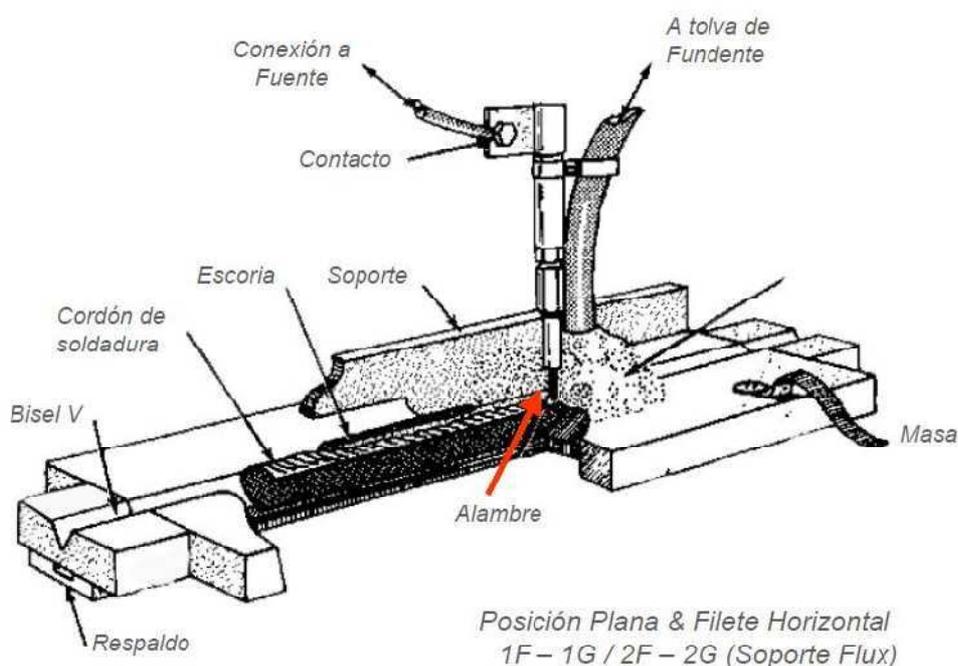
Proceso de Soldadura por Arco Sumergido
